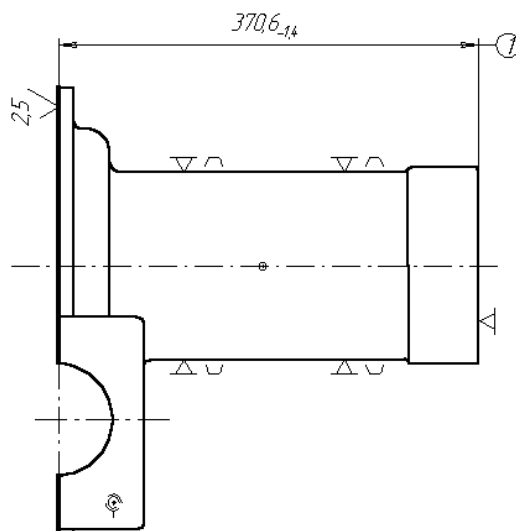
Операційний ескіз поздовжньо-фрезерної операції
